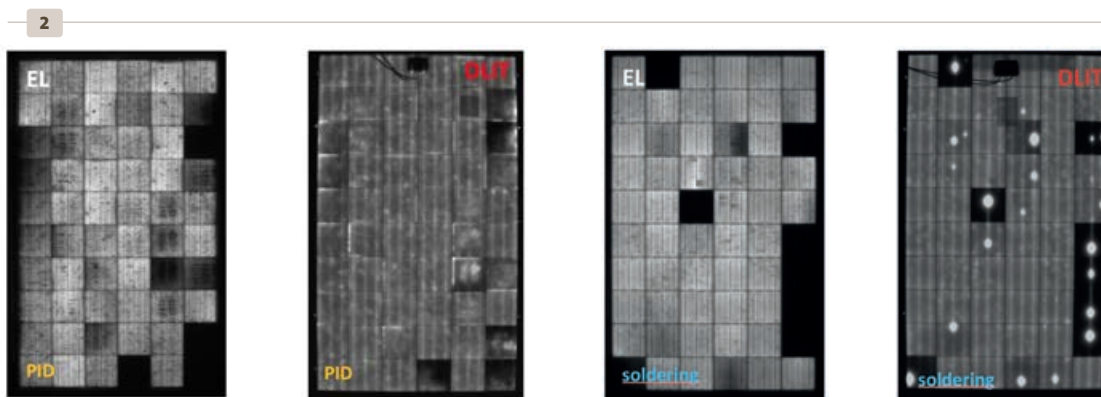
EL- und DLIT-Aufnahmen. Links: Modul mit PID; rechts: Modul mit Lötfehlern © aus [3]
